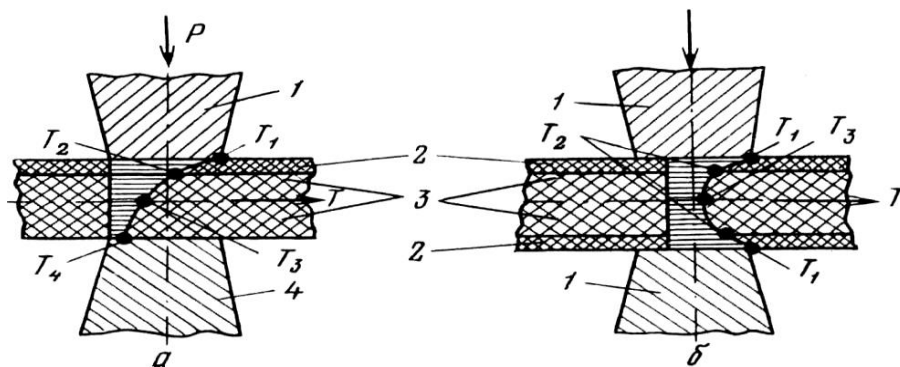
Схемы сварки нагретым инструментом косвенным нагревом нахлесточных соединений при одностороннем (а) и двустороннем (б) подводе тепловой энергии: 1 – нагретый инструмент; 2 – прокладка; 3 – свариваемые детали; 4 – холодный инструмент; $T_1 - T_4$ – распределение температур по толщине деталей
